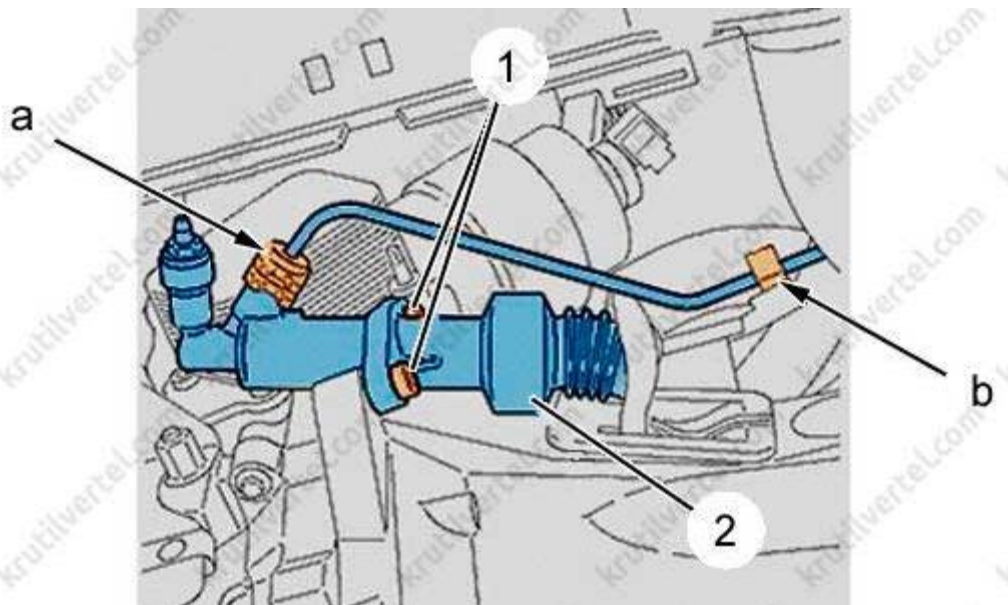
робочий циліндр зчеплення: 1 – кріпильні болти; 2 – корпус циліндра; a – підключення гідроприводу; b – скоба.
